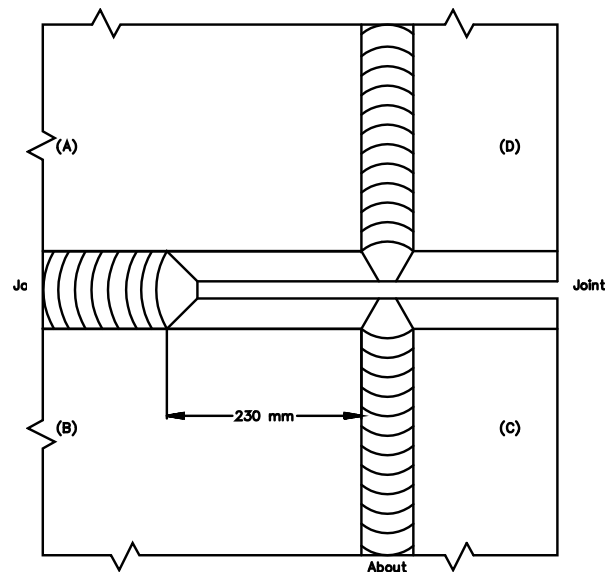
Séquence de soudage type pour la réparation du bordé extérieur
